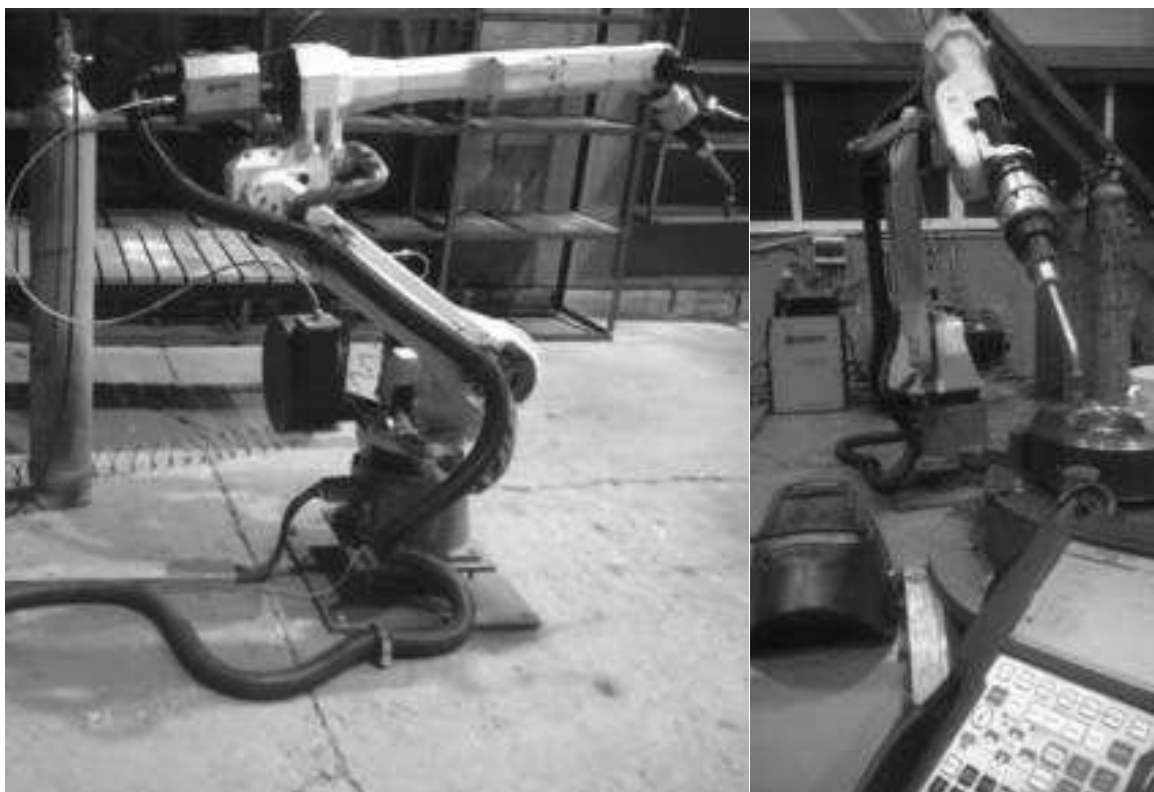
Сварочный робот M-201A 10L
